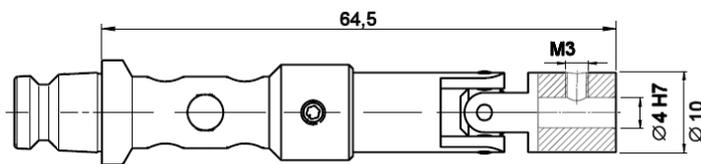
Adapter U2 mit Rotoren E100, E500, FL100 und FL1000
